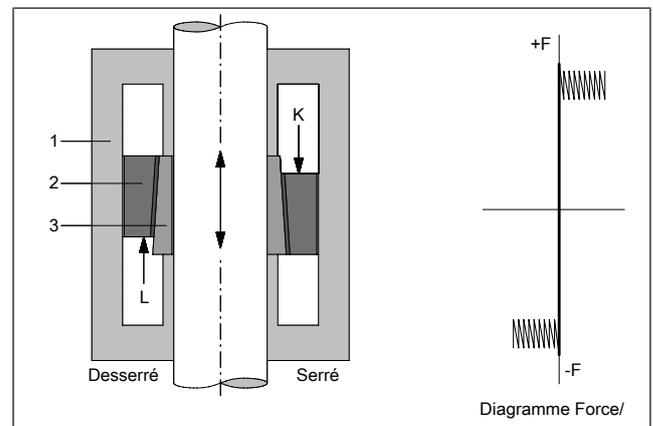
Principe de fonctionnement du dispositif de serrage SERRA
